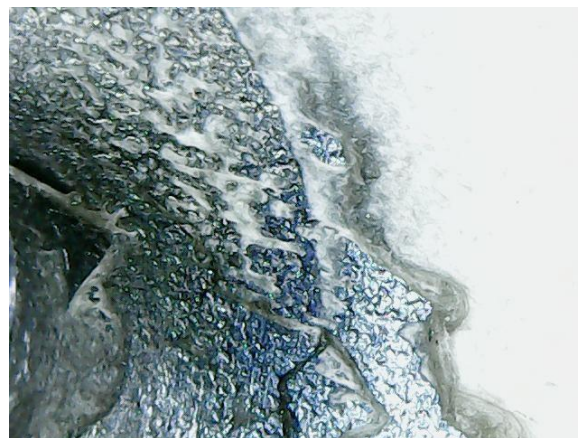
Фото поверхні заклепки (а) і околозаклепочной зони
